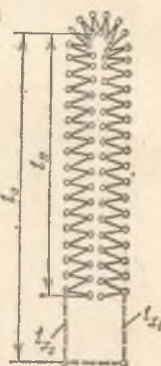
Схема изготовления петли на машине-полуавтомате двухниточной цепной строчки
